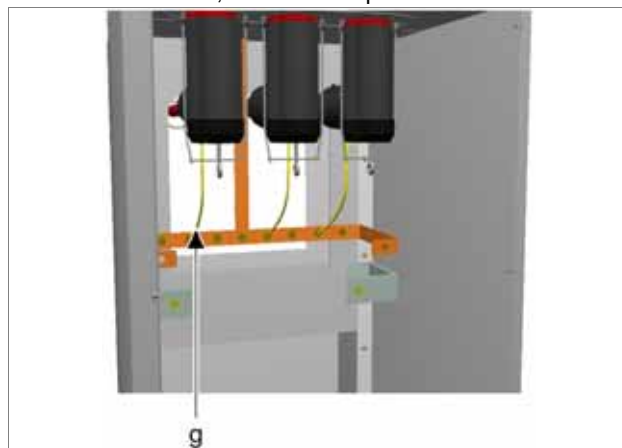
Conexión posterior en celdas modulares de 68 pulgadas (1.740 mm) de altura
